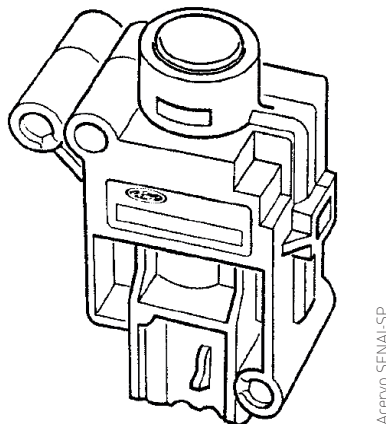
Interruptor inercial de corte de combustível (IFS).
